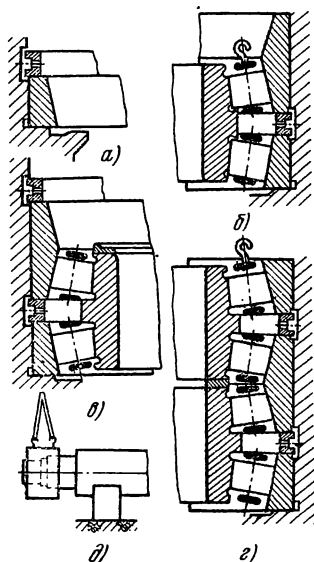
Последовательность монтажа четырехрядного роликового подшипника
